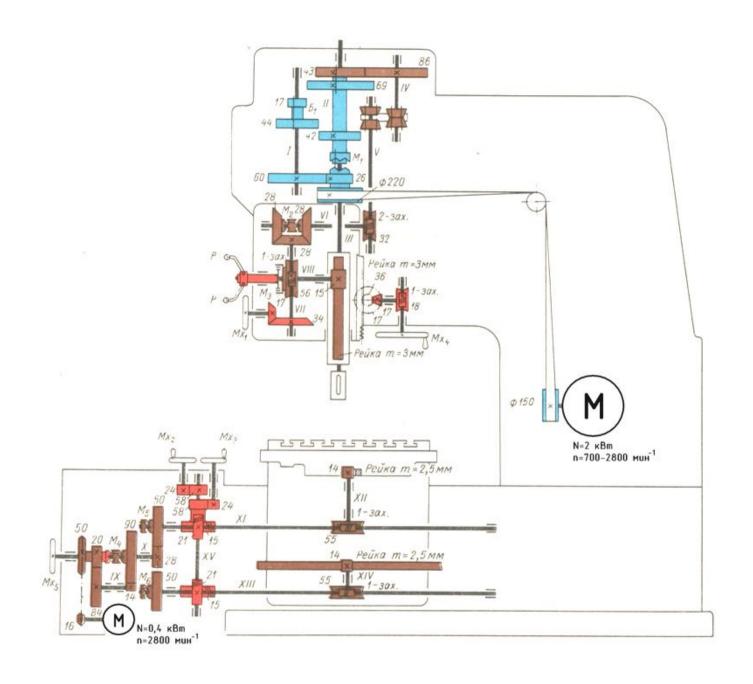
Кинематическая схема координатно-расточного станка модели 2450
